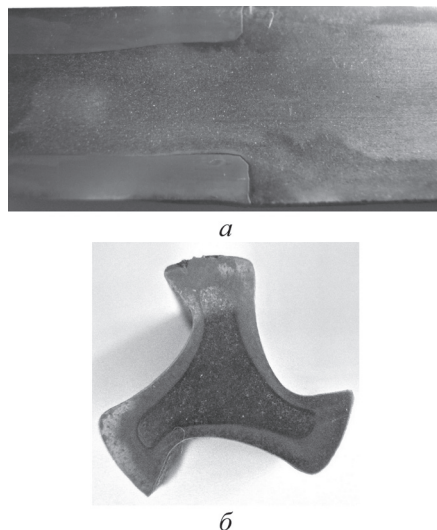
Продольный (а) и поперечный (б) разрезы биметаллической заготовки метчика машинно-ручного
